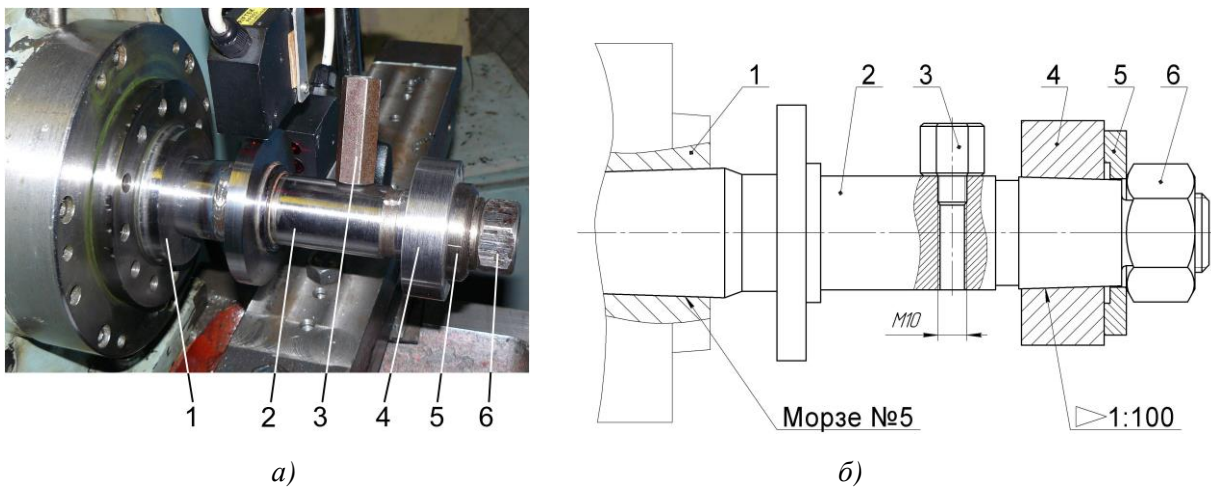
Загальний вигляд а) та ескіз б) прецизійної оправки: 1 – шпиндель; 2 – прецизійна оправка; 3 – змінний вантаж; 4 – оброблювана заготовка; 5 – шайба; 6 – гайка
